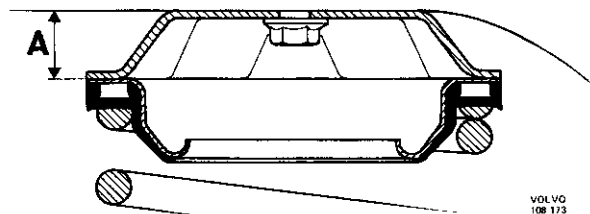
Obere Anschlagplatte für Hinterfeder
